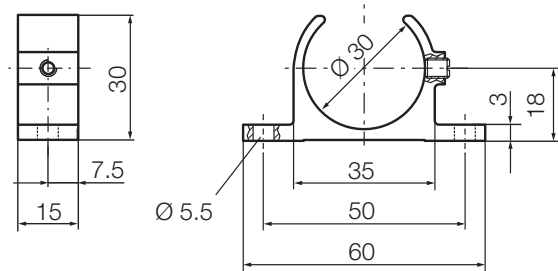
Befestigungsklammer BTL6-A-MF01-A-50
